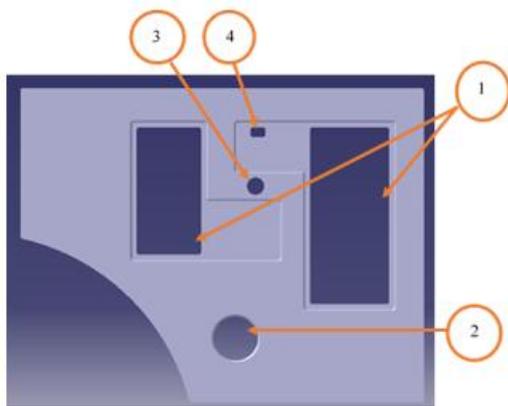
Inner Door Panel* Mobil *Pick-Up* GEA
